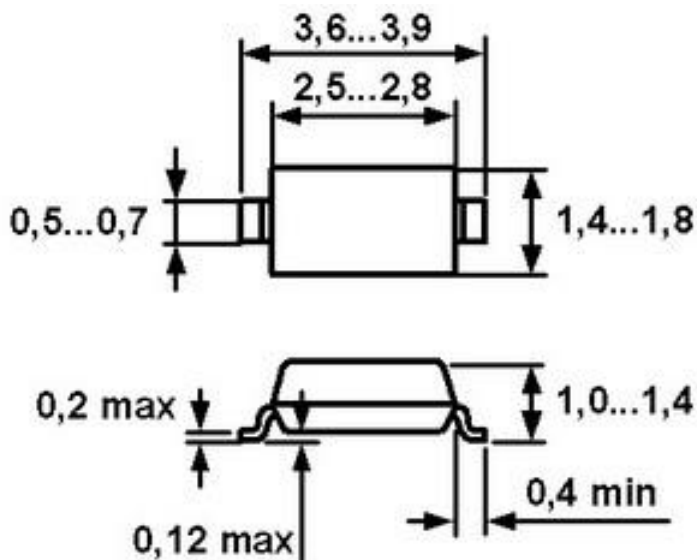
Габаритні розміри корпусу SOD-123
